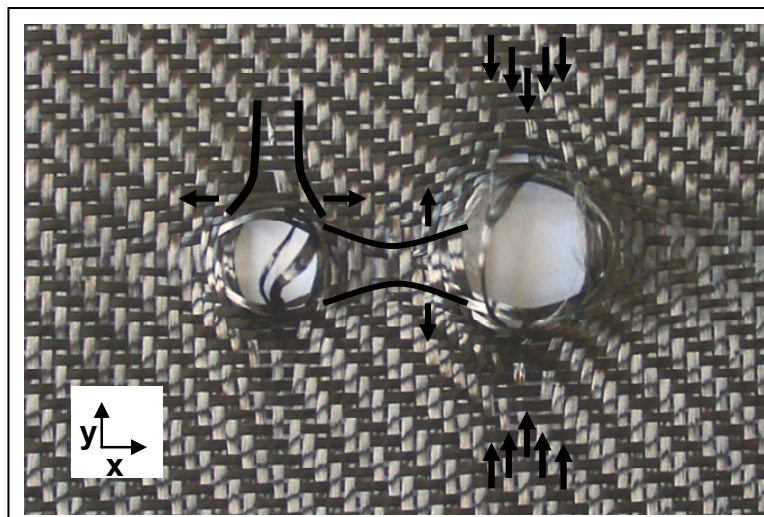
Faserorientierung nach der Drapierung zweier Formnester (CF-Körper 2/2 Gewebe)
